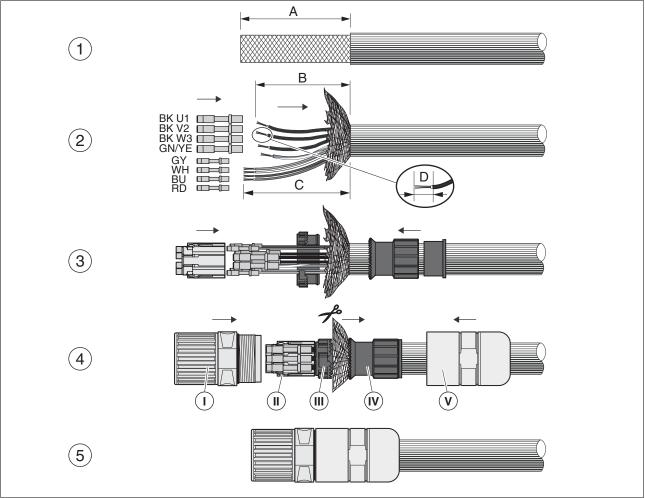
Assemblare il cavo motore con connettore motore M23
